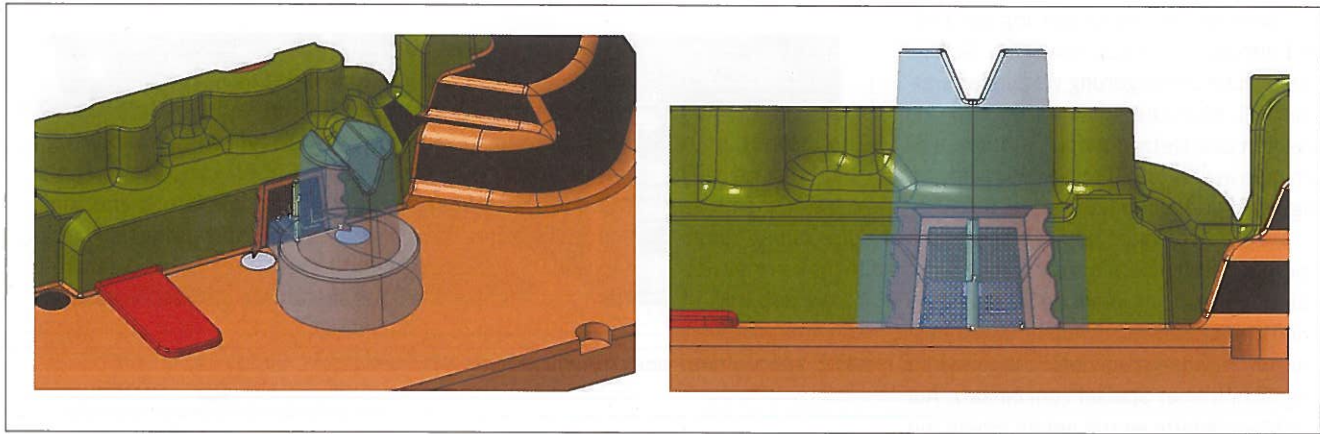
Positionierung des NETFrames an der Bauteiloberfläche mit speziellen Haltern.
